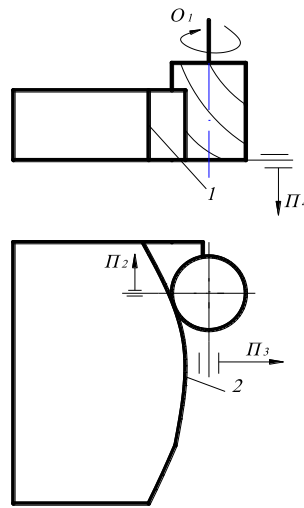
Схема фрезерування криволінійної поверхні кінцевою фрезою
